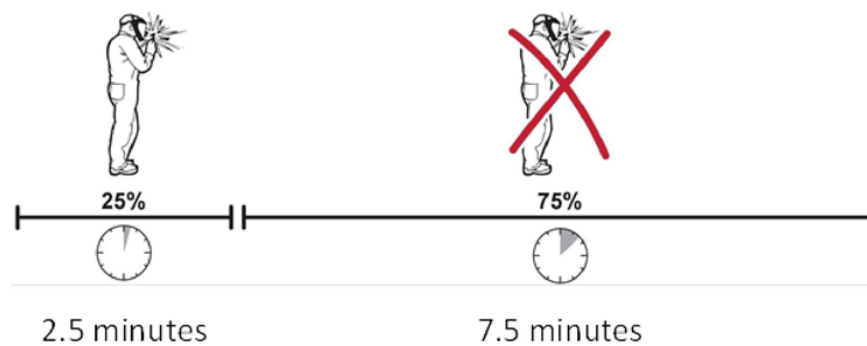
GTAW (AC TIG) 230 V Inschakelduur
